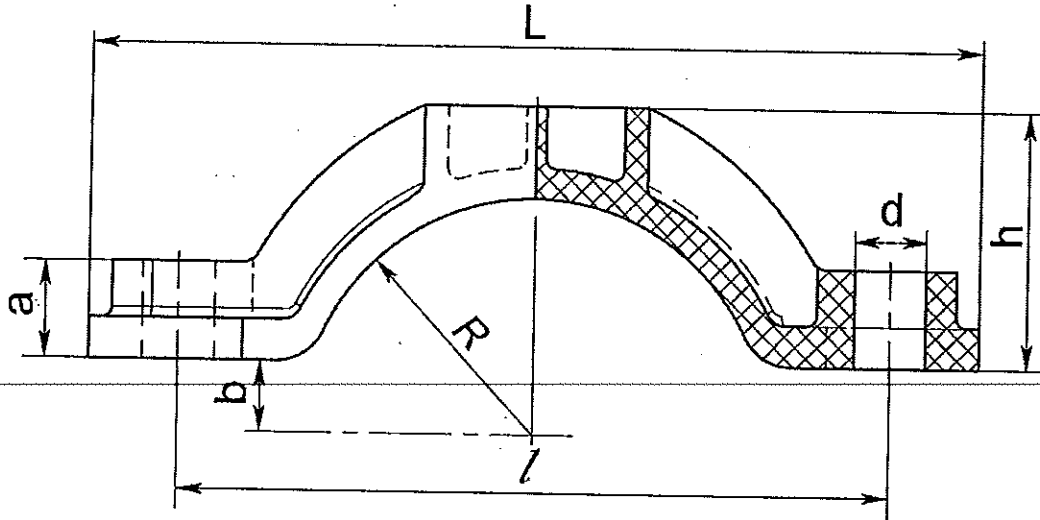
Габаритные размеры кабельных креплений типа ВКК
